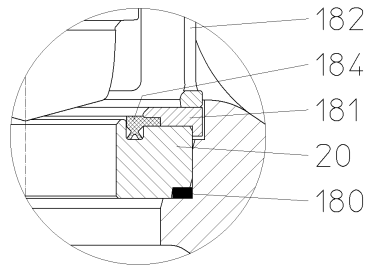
Weichabdichtung Flachdichtung & O-Ring - Detail Y
